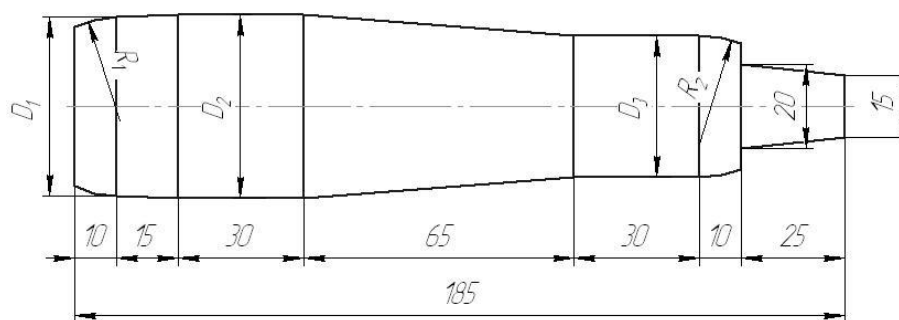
Калибровка оправки лабораторного стана «УралНИТИ» для исследования процесса риллингования с уменьшением диаметра трубы
